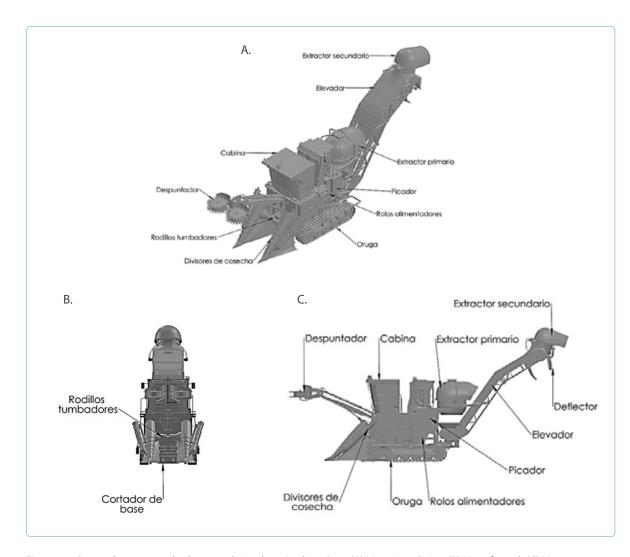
Partes de una cosechadora mecánica de caña de azúcar: (A) Vista isométrica, (B) Vista frontal, (C) Vista lateral.
